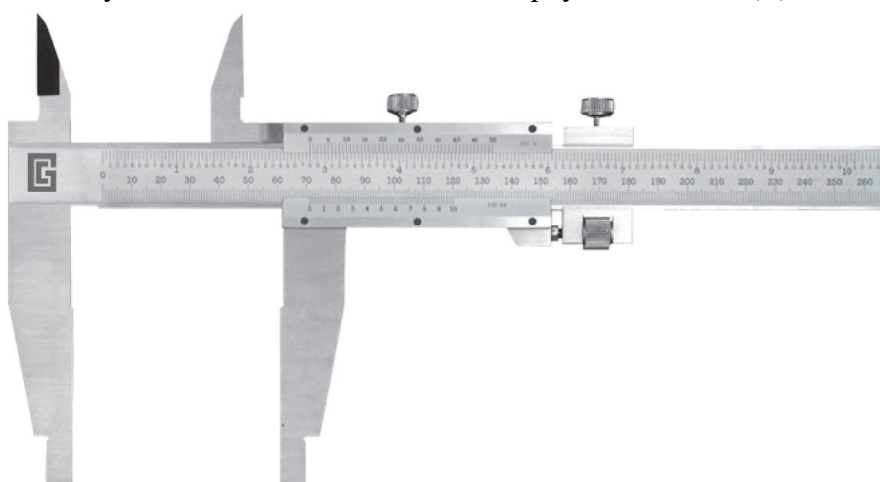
Общий вид штангенциркулей типа ШЦ-V.
